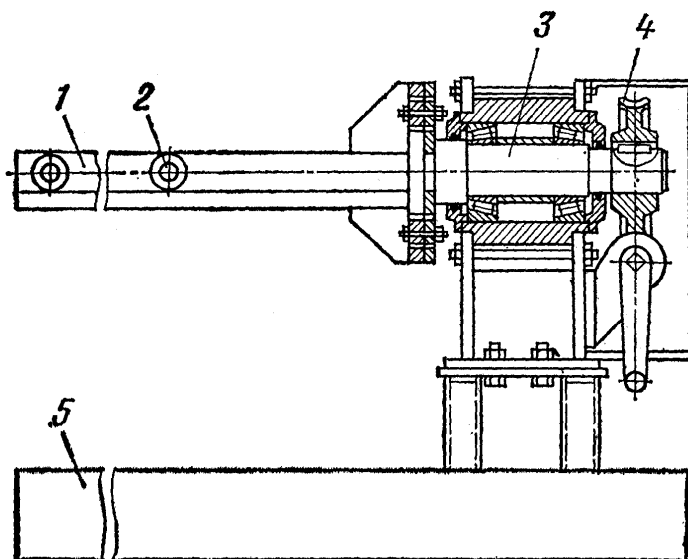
Стенд для розбирання двигунів вилючної конструкції
